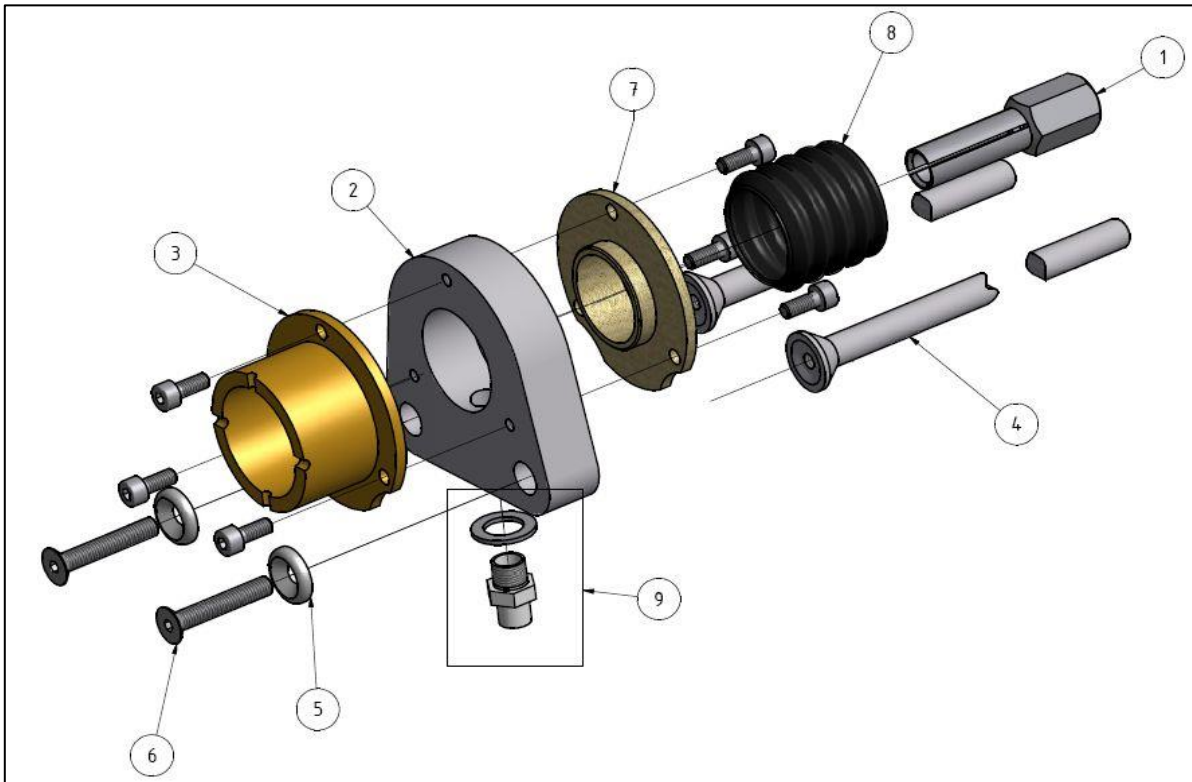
Stützeinrichtung für das Schutzgasbolzenschweißen (Pistole K 22)
